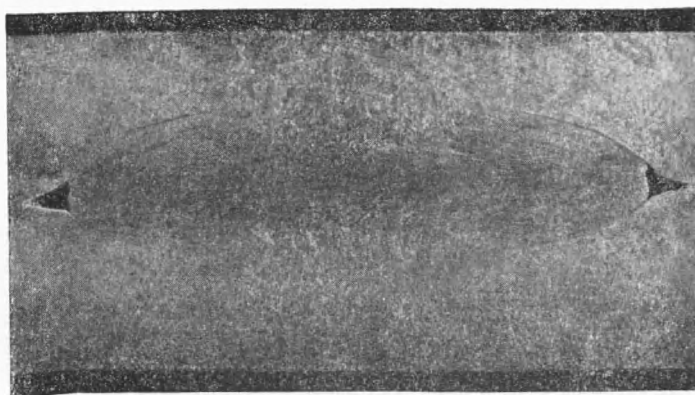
Шлиф зоны соединения, полученного при деформировании двух цилиндрических (с цилиндрическими выступами меньшего диаметра) образцов из меди. $\times 5$
